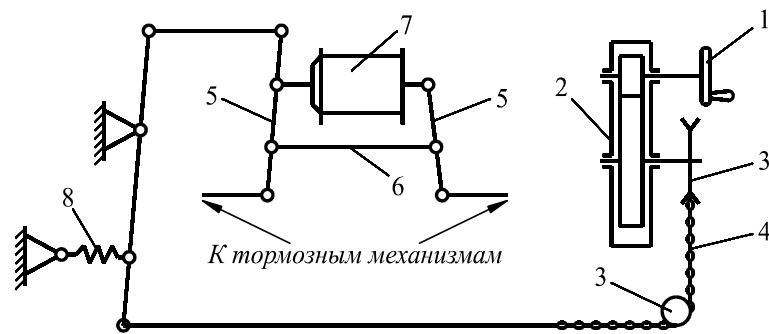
Схема редукторного привода стояночного тормоза:
